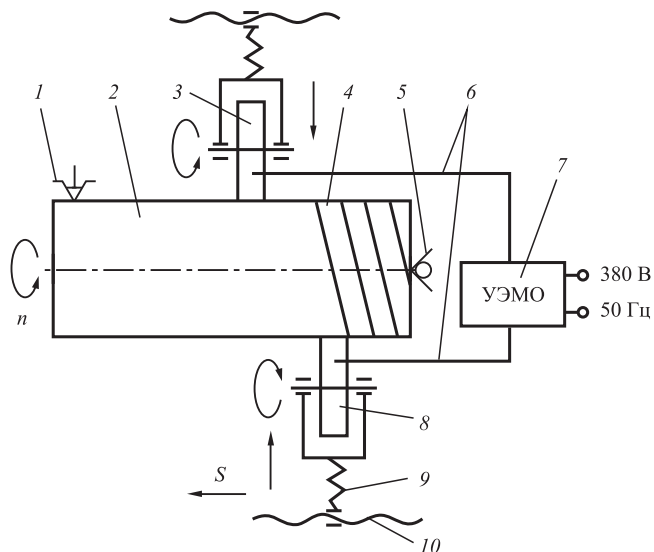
Принципиальная схема ЭМО заготовки на токарно-винторезном станке:
